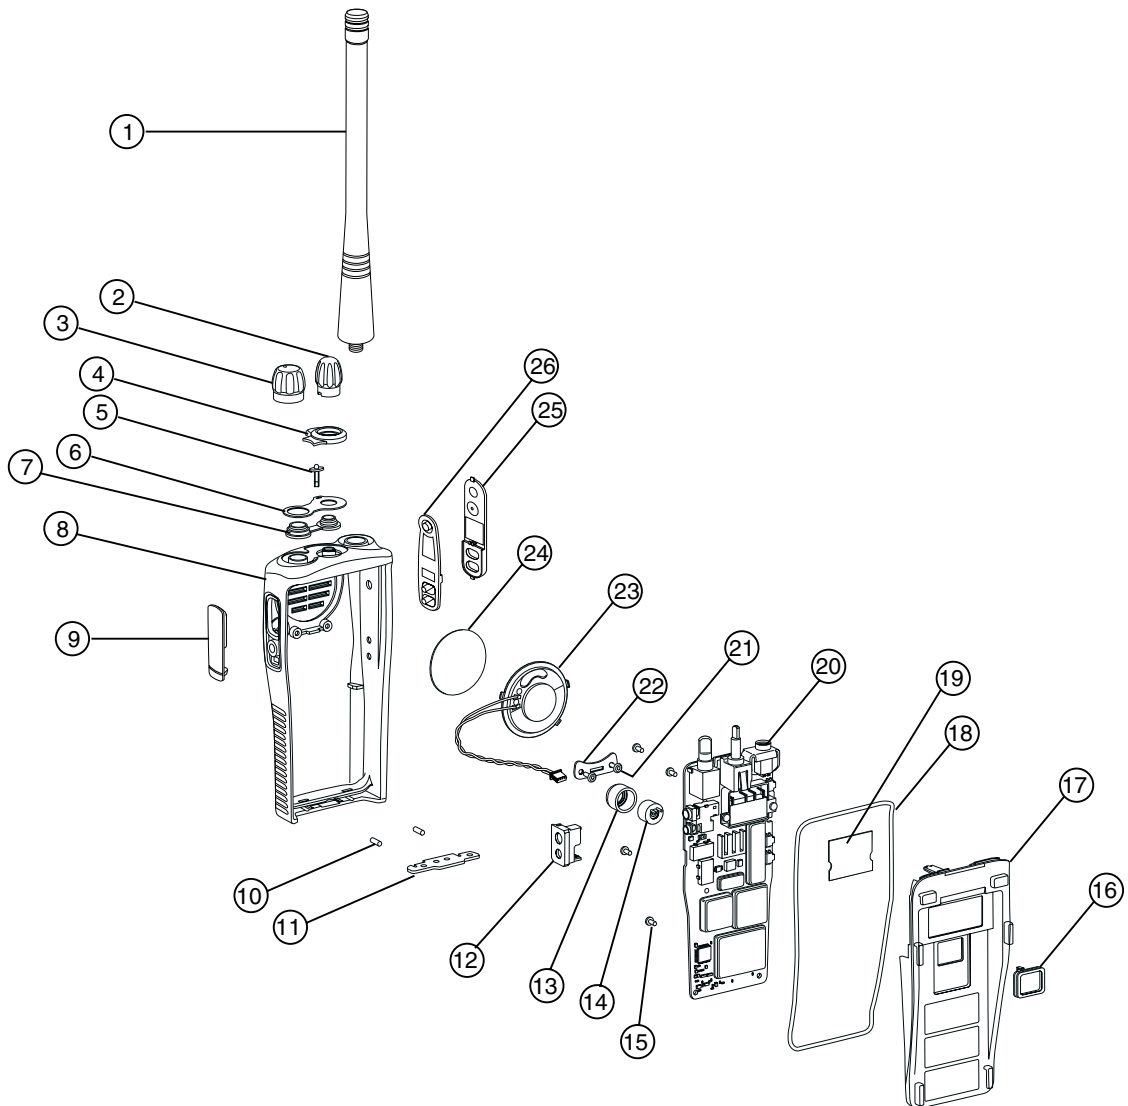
CP040 Funkgerät - Explosionszeichnung
